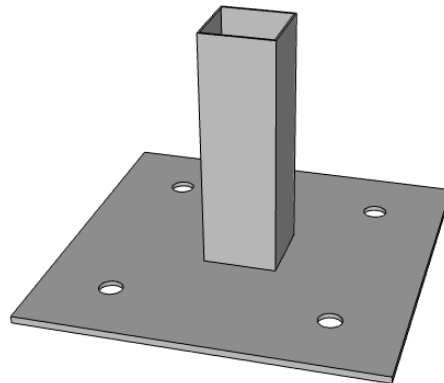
Base de fijación al suelo del toldo soldado
